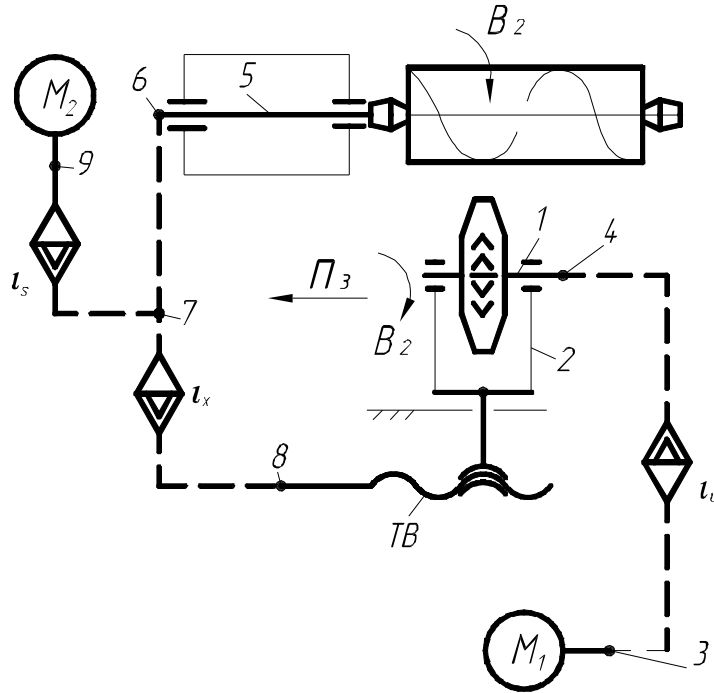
Типовая структурная схема резьбофрезерного станка
